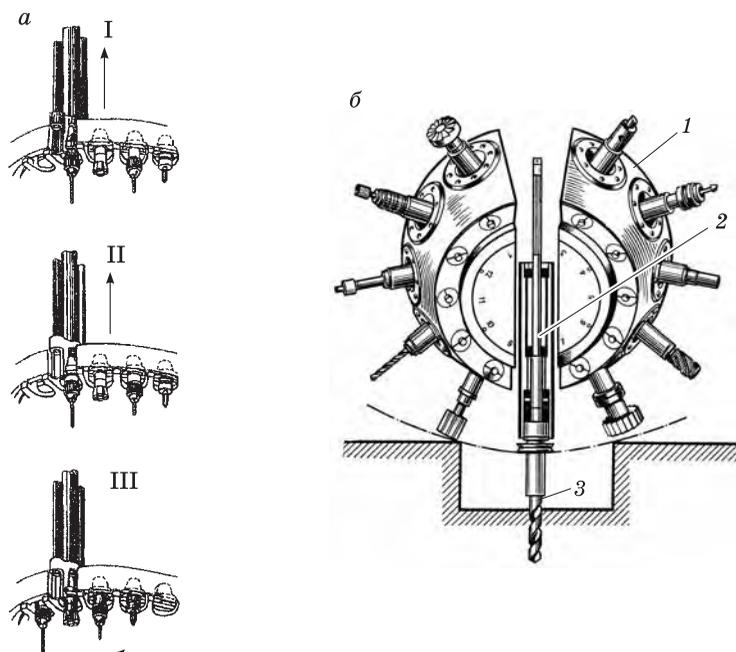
Устройства для смены инструмента осевым перемещением шпинделя
